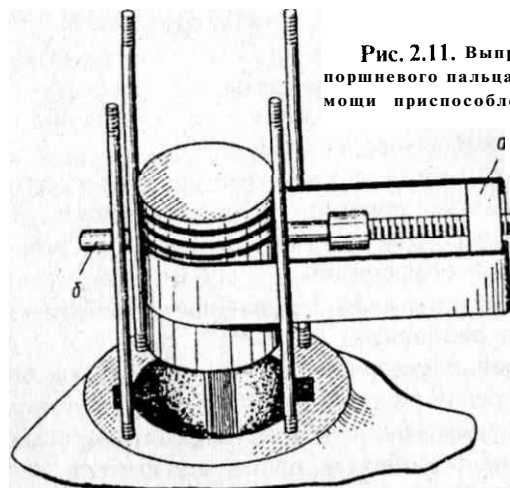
Выпрессовка поршневого пальца при помощи приспособления
